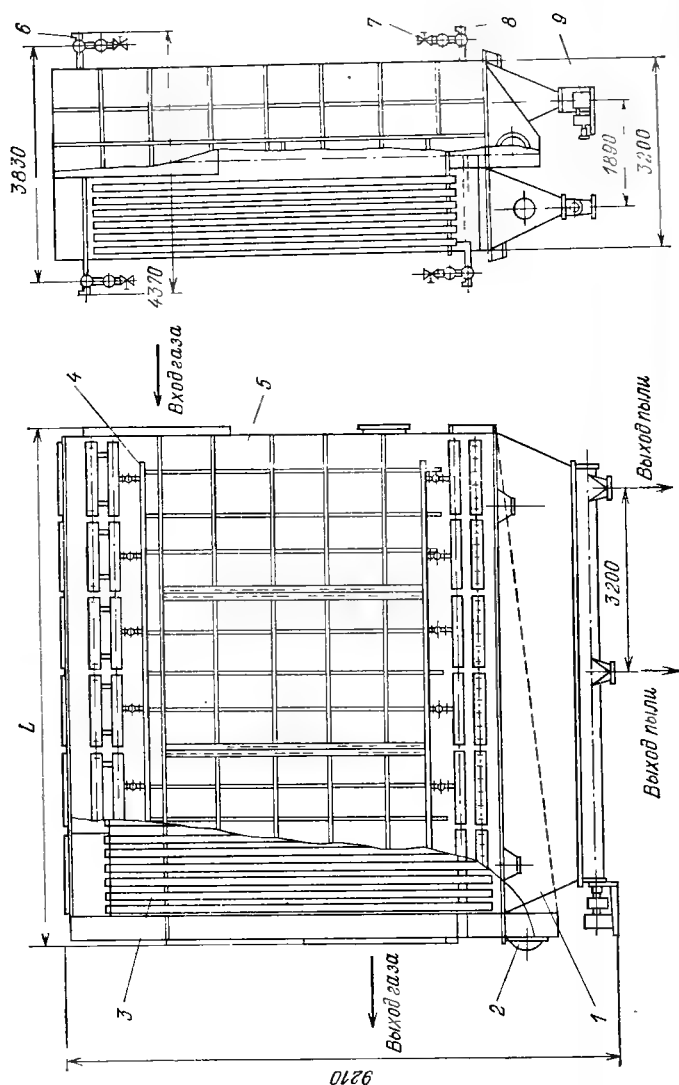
Рукавный фильтр типа ФРКДИ
